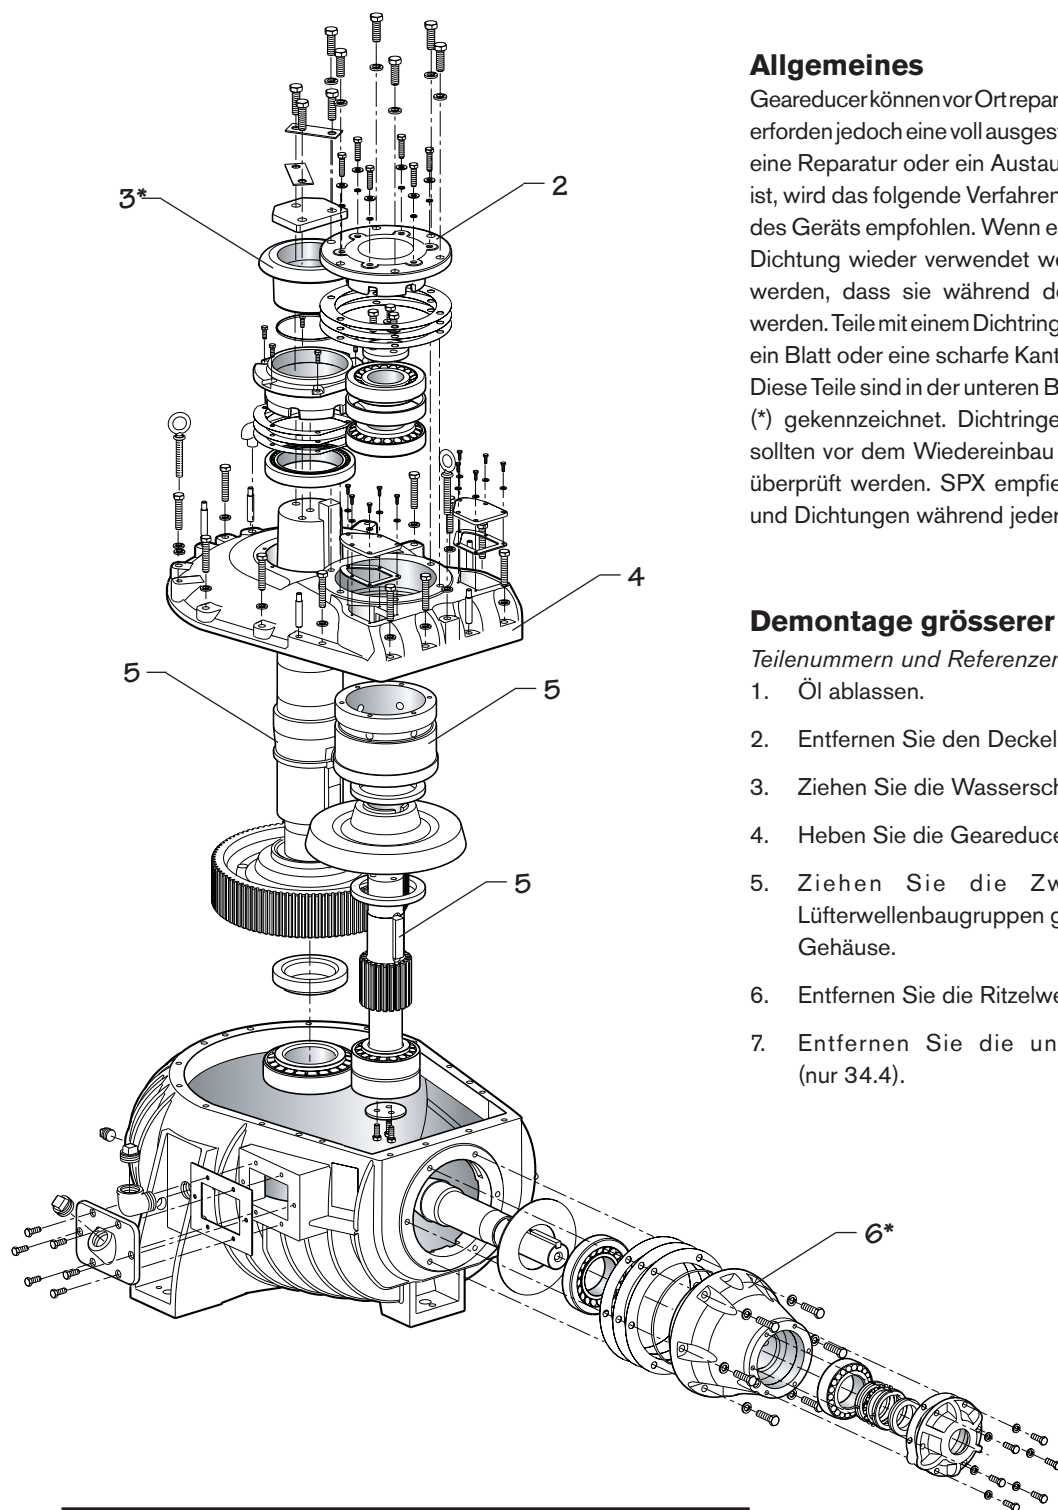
Modell 34.4 Explosionszeichnung der Baugruppe
